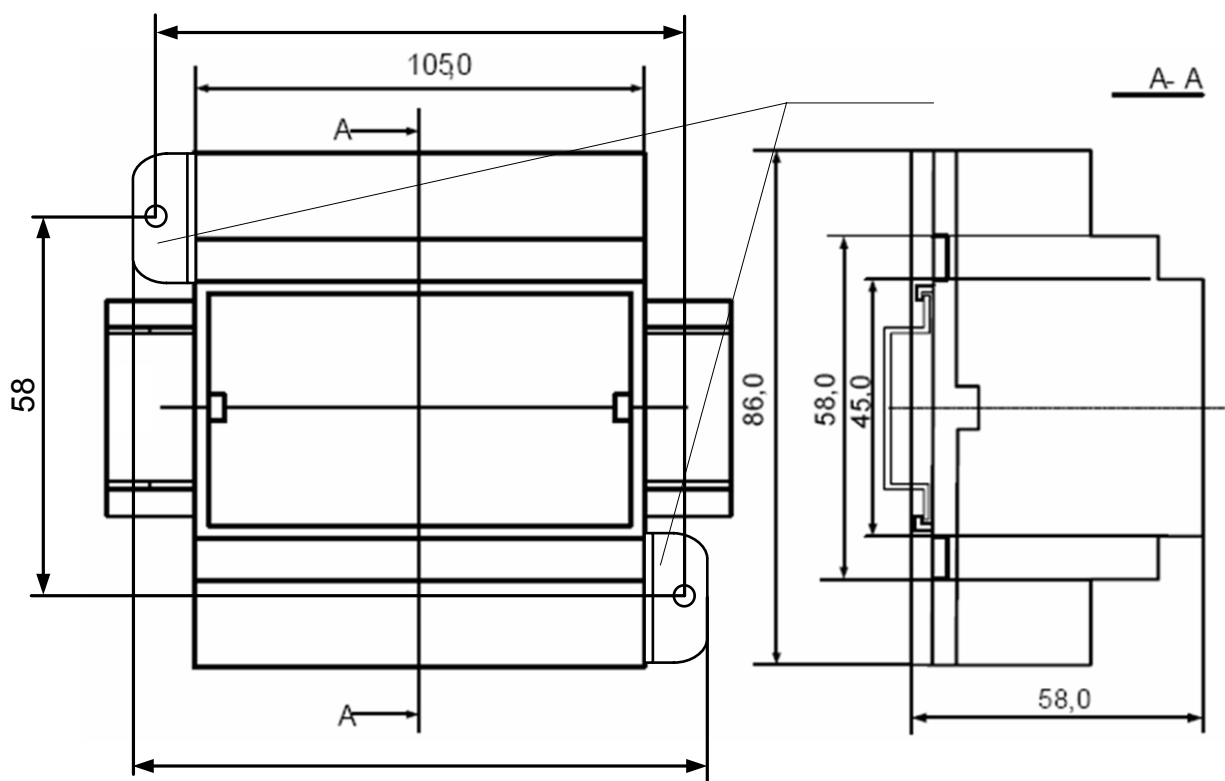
Габаритные и присоединительные размеры блока питания и реле PSM/4R-36-24
